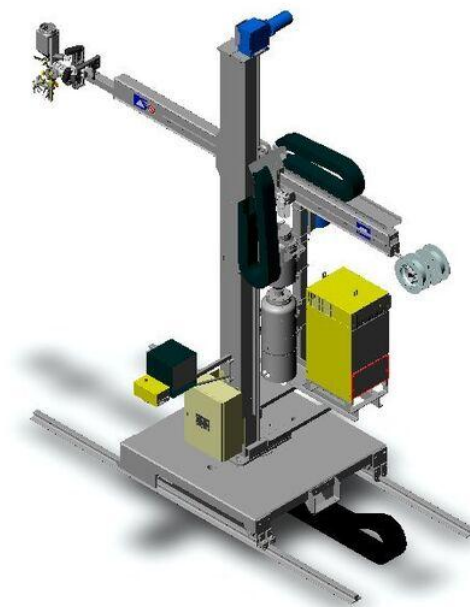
Зварювальний комплекс ESAB CaB 300M [18]
